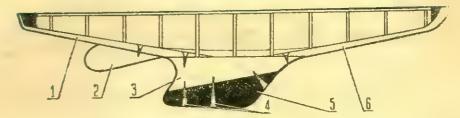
Килевая рамка: 1 — вилевой брус; 2 — плавинк; 3 — киль; 4 — шуруны; 5 — свинцовый фальшкиль; 6 — килевой брус.
